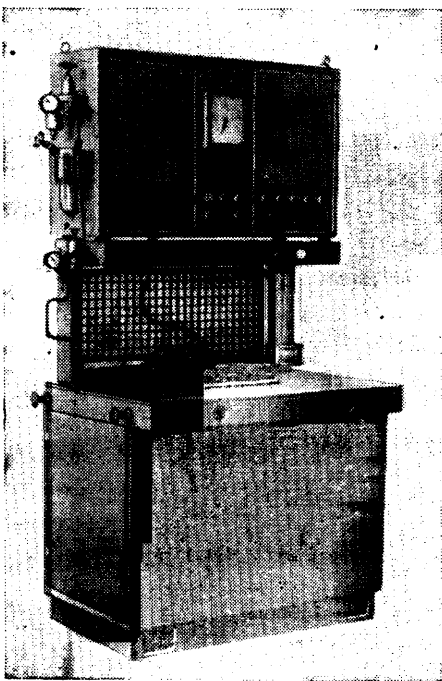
Полуавтомат для испытания на герметичность корпуса клапана включения делителя передач
